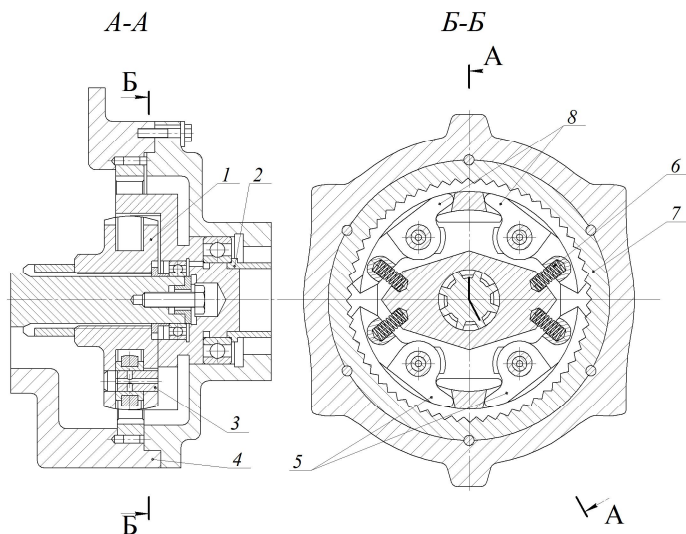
Храповой останов для ограничения обратного силового воздействия на ручной привод: 1 – храповая втулка; 2 – ведущий вал; 3 – ось; 4 – корпус; 5 – храповой рычаг; 6 – пружина; 7 – храповое колесо; 8 – храповой рычаг
